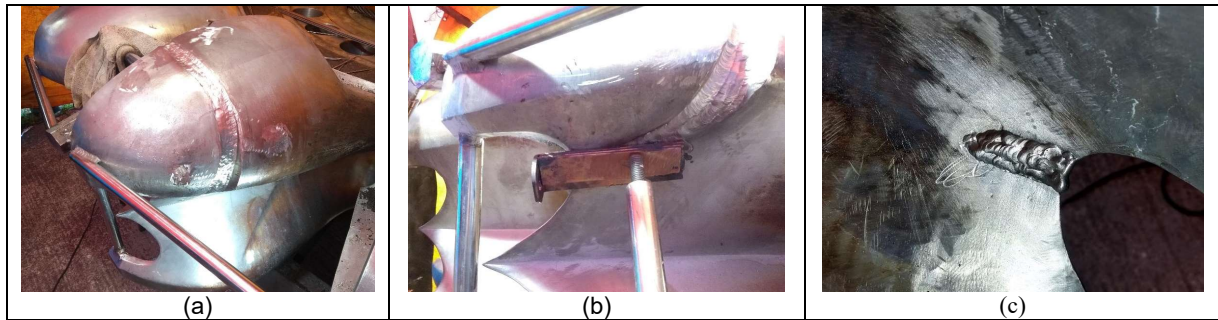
Posicionamento do cobre-junta durante a soldagem da borda frontal da concha.
